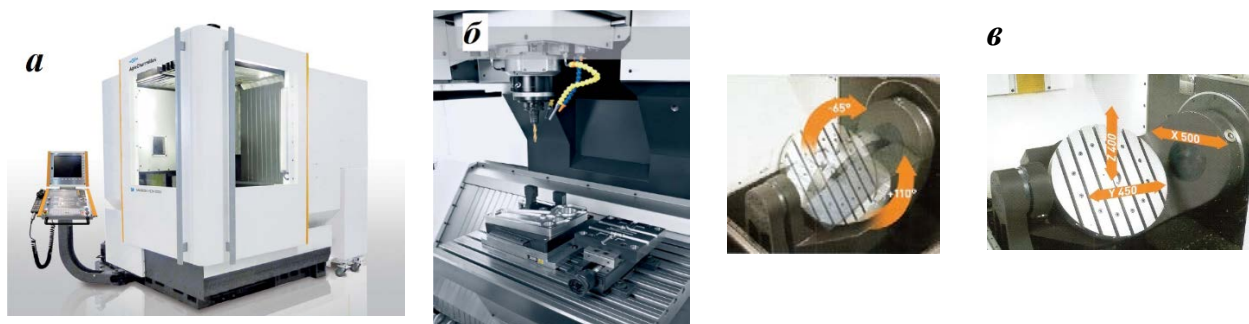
Обрабатывающий центр с ЧПУ Mikron NEM 500U: а – общий вид; б - встроенный шпиндель; в - поворотно – наклонный стол с параллельными пазами
